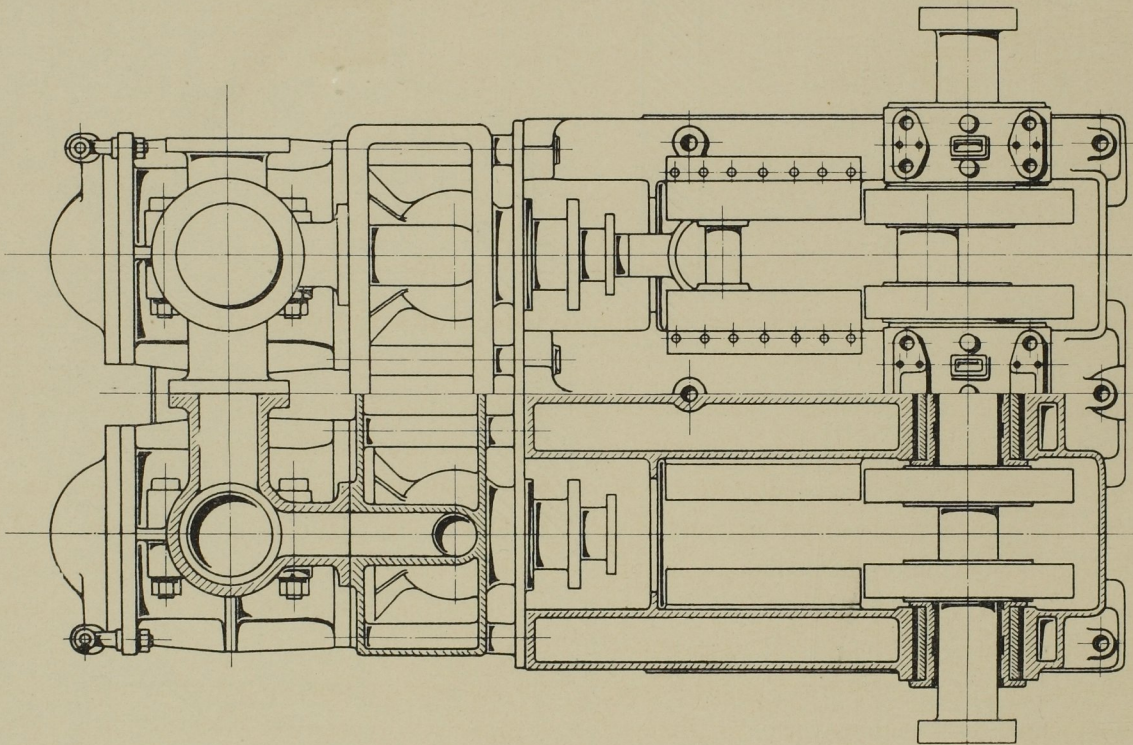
Grundriss der Pumpe. Massst. 1 : 15.
